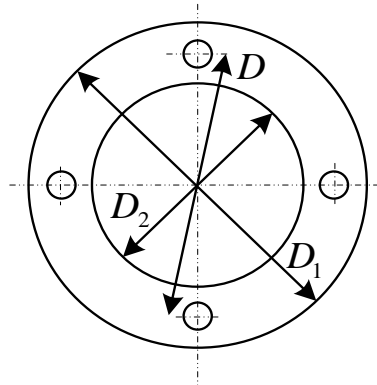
Схема для расчета соединения в виде кольцевого стыка
